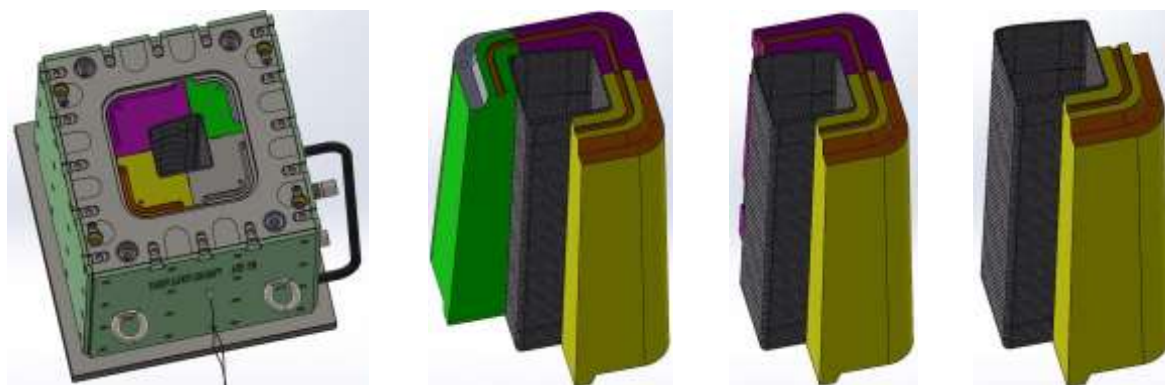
Diseño de molde RTM para la fabricación de pieza hueca aeronáutica, desarrollado en Eurecat.
